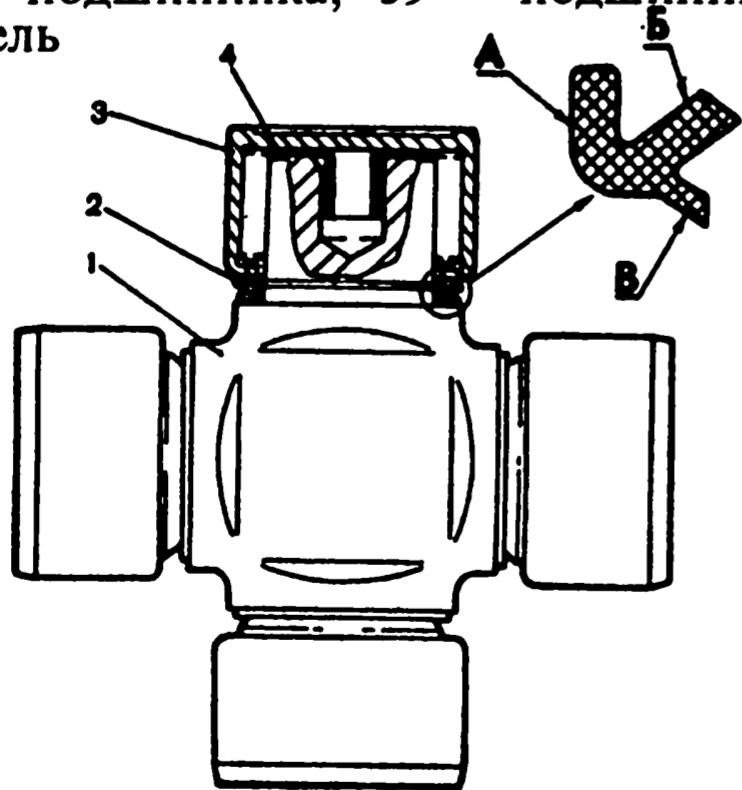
Крестовина карданного шарнира в сборе: 1 - крестовина; 2 - сальник радиально-торцевого уплотнения; 3 - игольчатый подшипник; 4 - торцевая шайба; А, В - уплотнительные поверхности сальника
